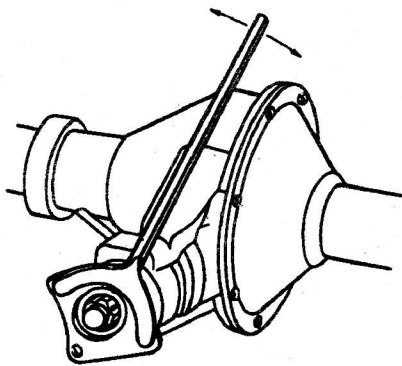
Удерживание фланца вилкой 7811-4612 при затягивании гайки ведущей шестерни
